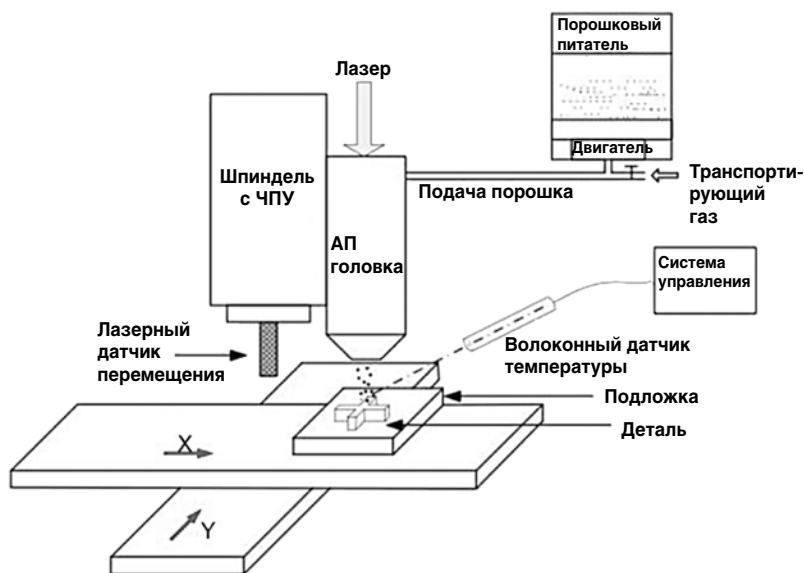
Конструкция типowego гибридного станка, оснащенного фрезерным шпинделем и головкой для лазерной наплавки
